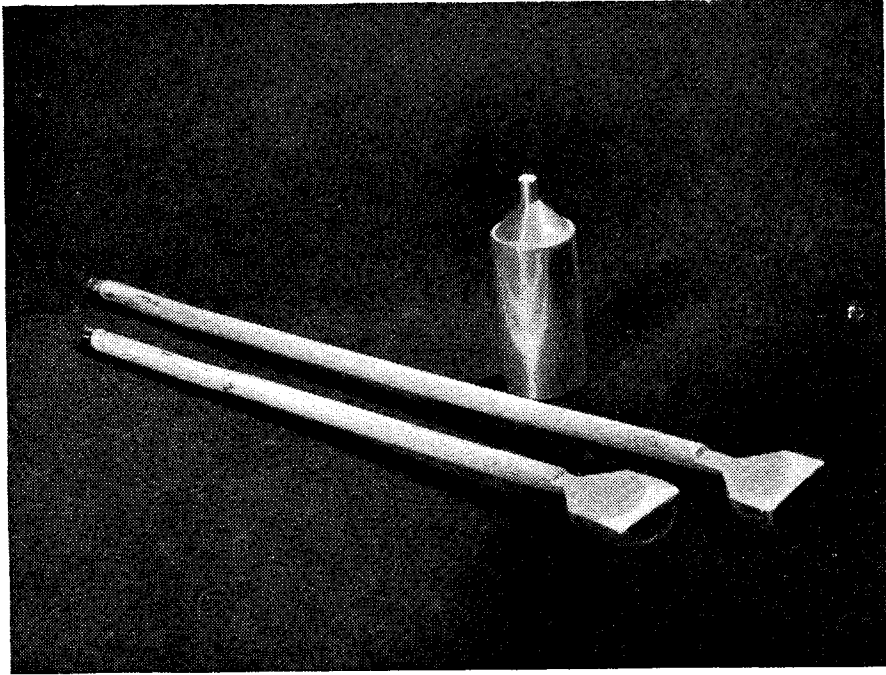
Vista de un tocho listo para extrudar y dos etapas durante el proceso de extrusión.
